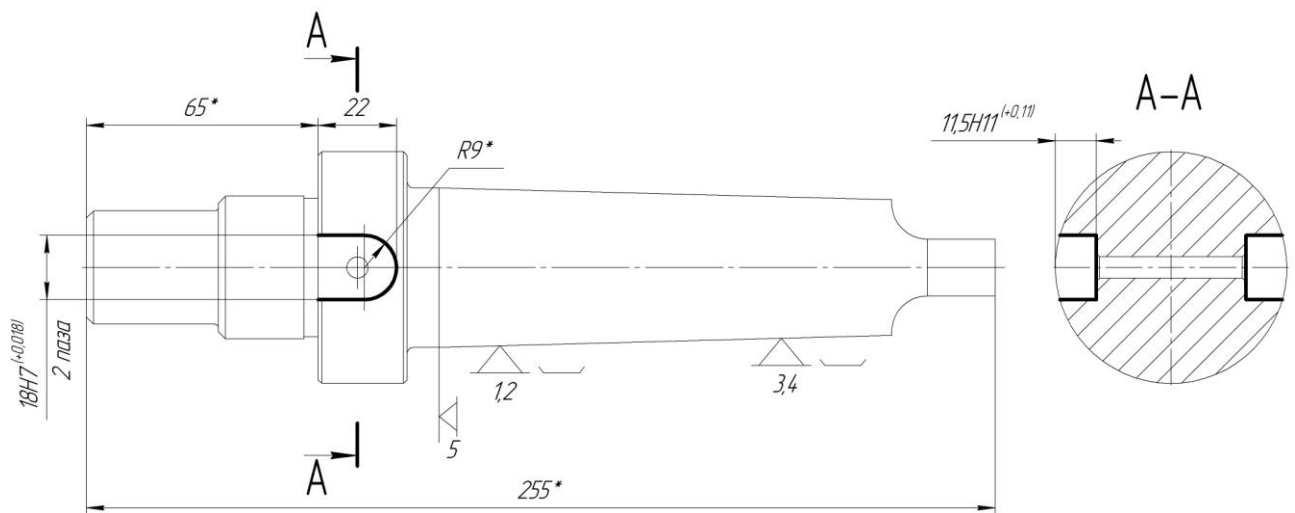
Схема базування заготовки на координатно-розточувальній з ЧПК операції (перший варіант)
